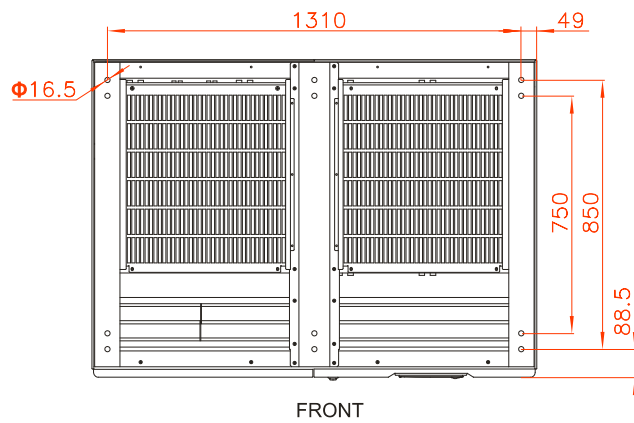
Монтажная рама с размерами для FR-UK(/B)33(200-250) (вид сверху)
